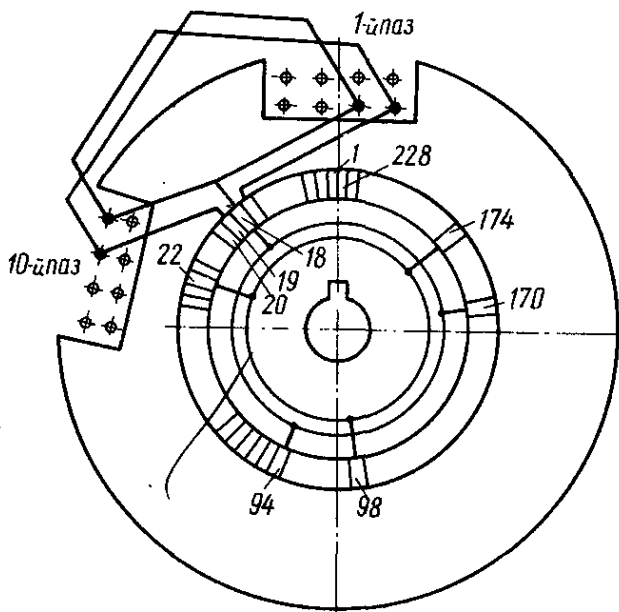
Схема сердечника обмотки якоря с коллекторными пластинами генератора НБ-429А (НБ-436А)
